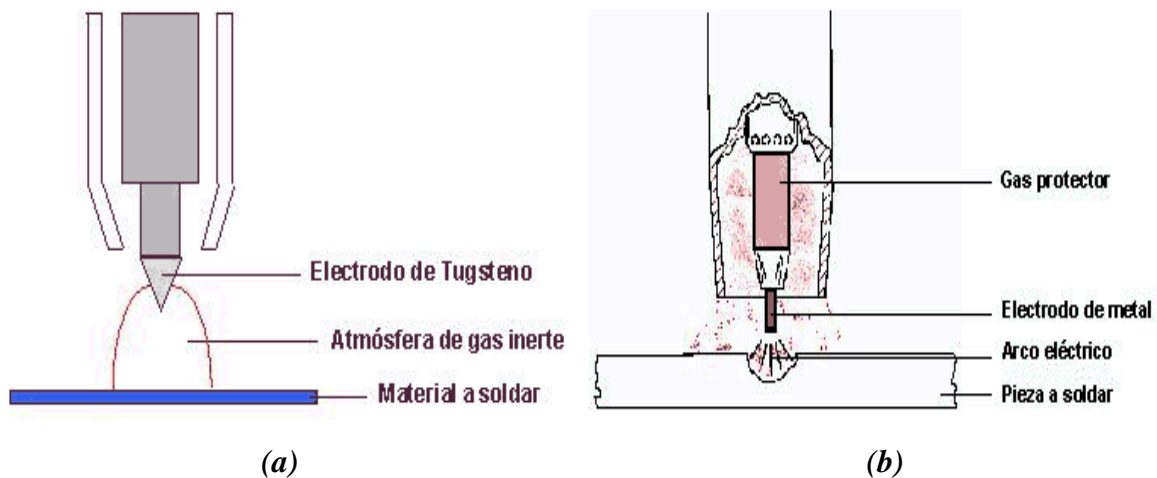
Esquema de las soldaduras por fusión: (a) TIG, y (b) MIG.
